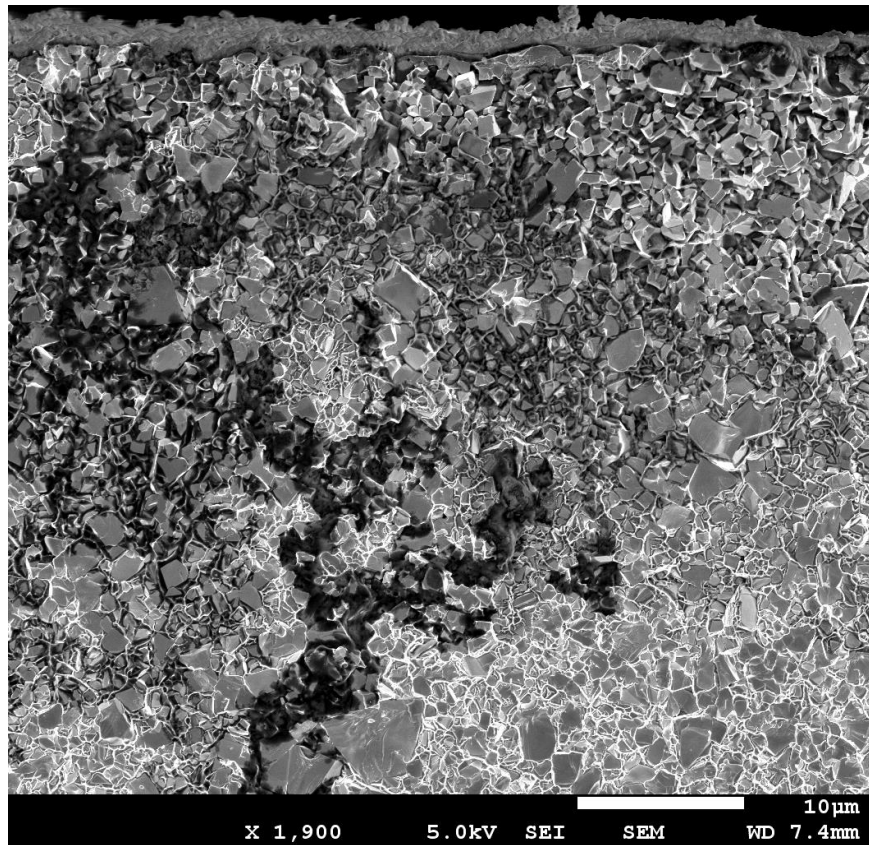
GD13. El origen de la fractura es una zona pobre en ligante.
